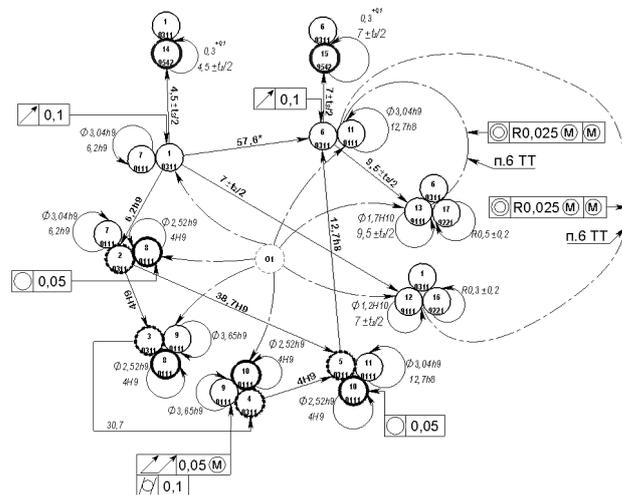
Граф размерных связей между элементарными поверхностями детали «Цанга», насыщенный информацией о конструкторских базах детали
